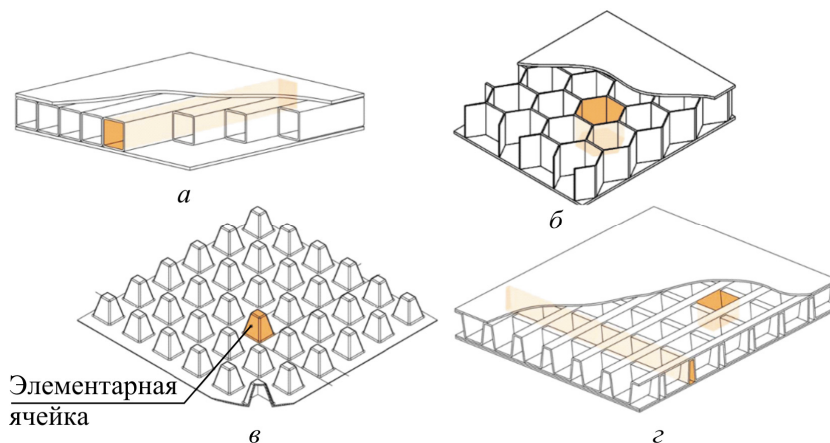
Звукопоглощающие конструкции: *а* – ЗПК с трубчатым наполнителем; *б* – ЗПК с наполнителем в виде сотовой конструкции; *в* – ЗПК с пирамидальным наполнителем; *г* – ЗПК с наполнителем из гофрированных профилей [2]
